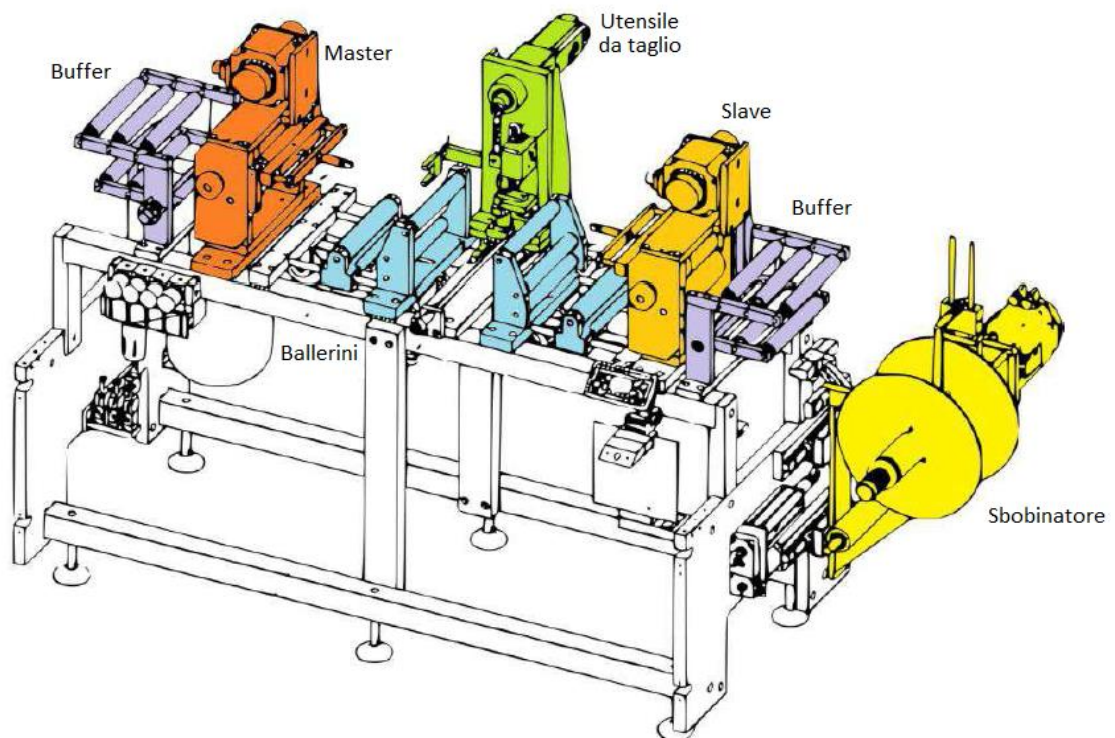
Vista in 3D della macchina di taglio al volo
